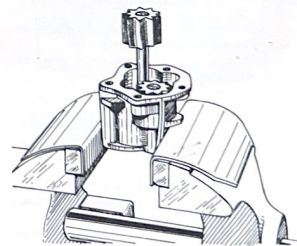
Extracción del eje de mando de la bomba con el engranaje conductor.
